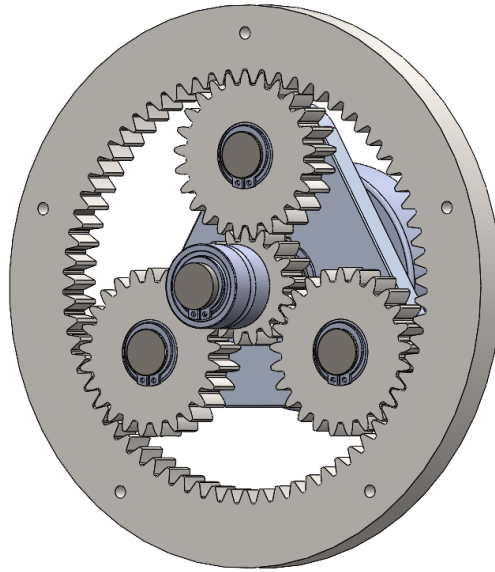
Ensamblaje CAD 3D de la caja de engranajes desde la perspectiva del eje de entrada.
